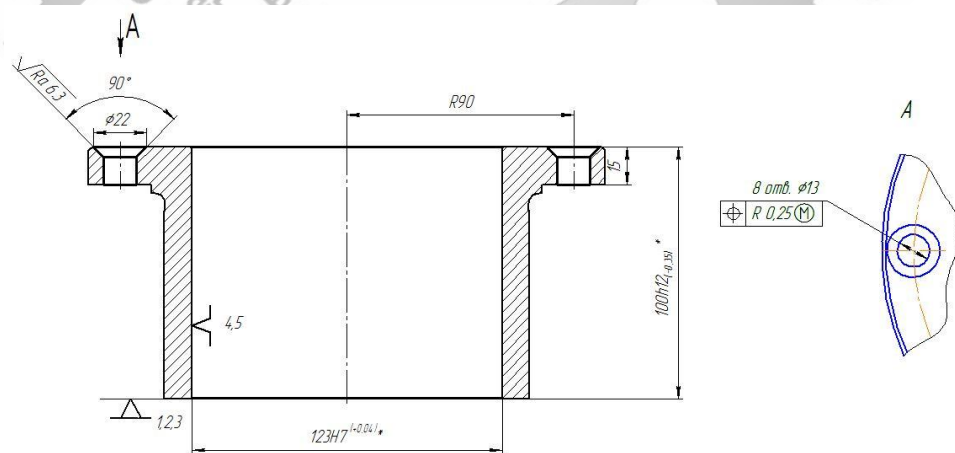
Схема базування деталі на оправці на операції 040 (свердильна з ЧПК)
